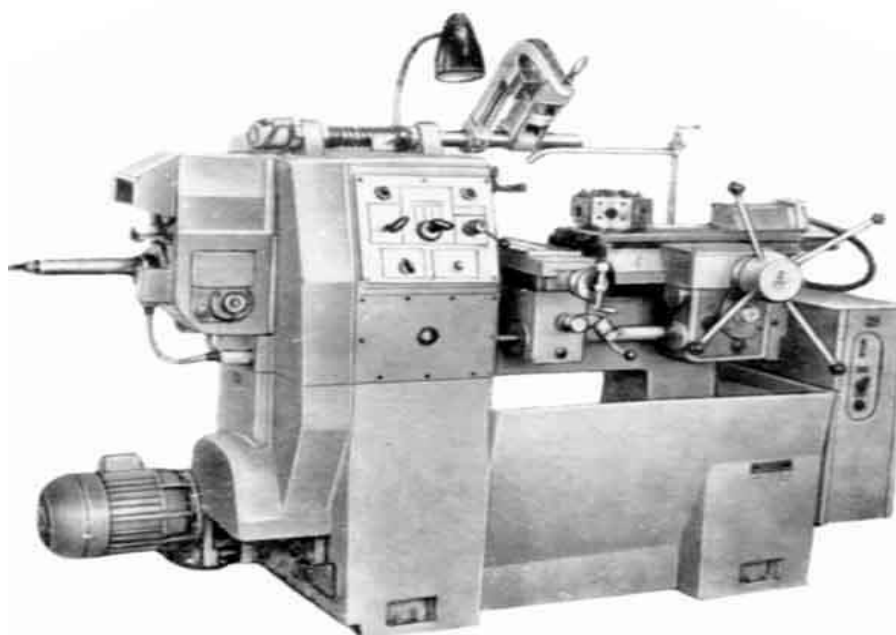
Токарно-револьверный станок модели 1Н318
